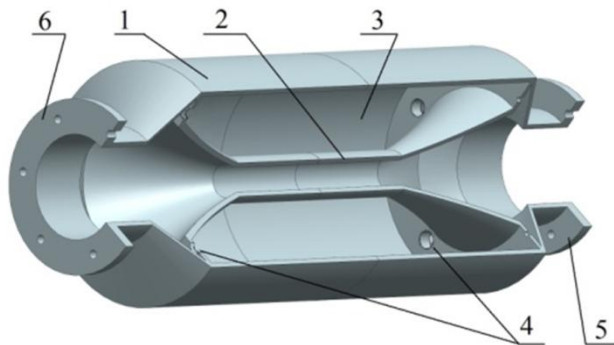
Схематическое изображение гасителя колебаний: 1 – корпус гасителя колебаний в сборе; 2 – зауженный канал; 3 – непроточная ёмкость; 4 – гидравлическое сопротивление; 5,6 – соединительные фланцы
